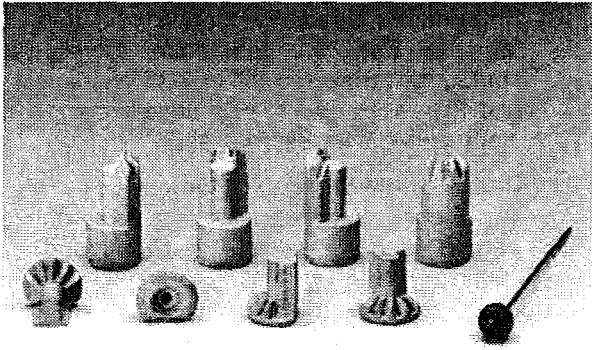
Korrosionsbeständige Zahnräder für eine elektrische Zahnbürste (Schunk Sintermetalltechnik GmbH, Gießen).
